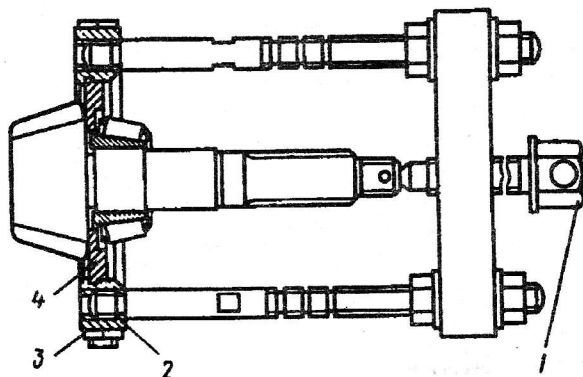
Снятие подшипника с ведущей шестерни главной передачи:
